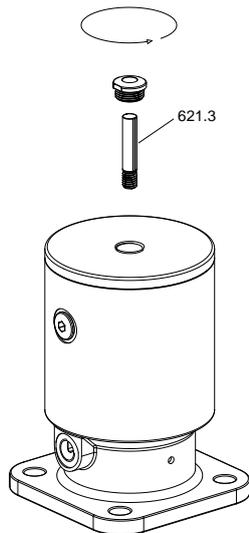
Smontaggio del tappo e dell'indicatore di posizione LAP.520/530
